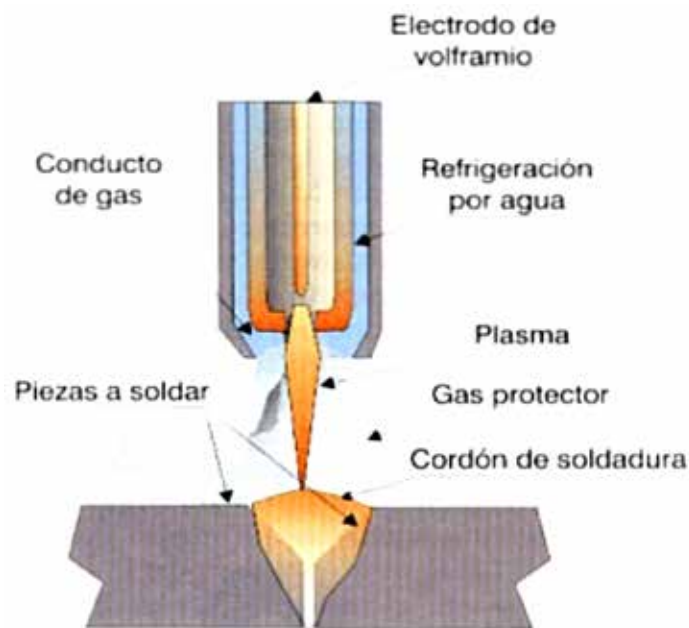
Soldadura con electrodo refractario (método TIG).
